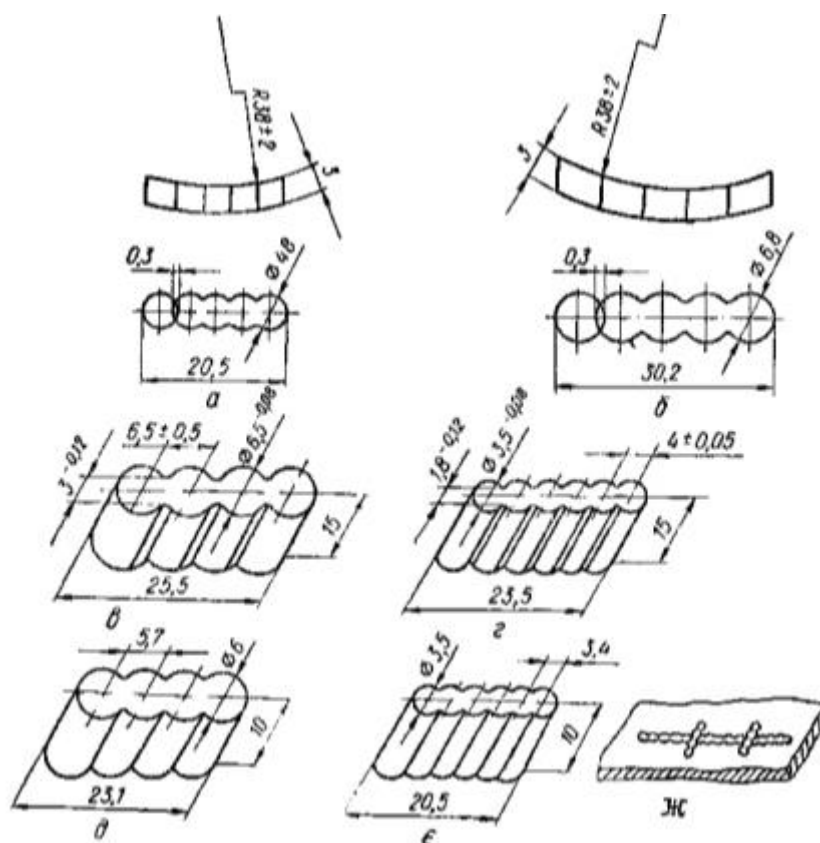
Стяжки і вставки для ремонтування корпусних деталей із тріщинами: а, б – ущільнювальні; в, г, д, е – стягувальні; ж – схема свердління отворів під вставки
